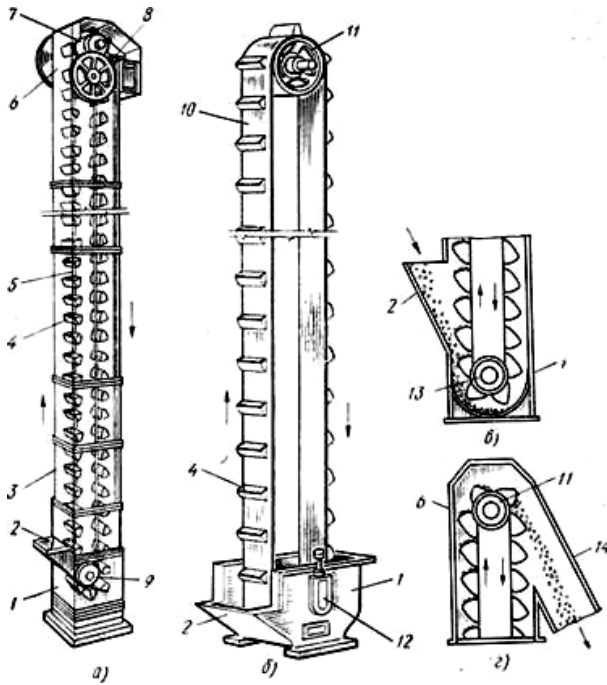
Ковшовые элеваторы: а — цепной; б — ленточный; в) — загрузка; г) — разгрузка:
